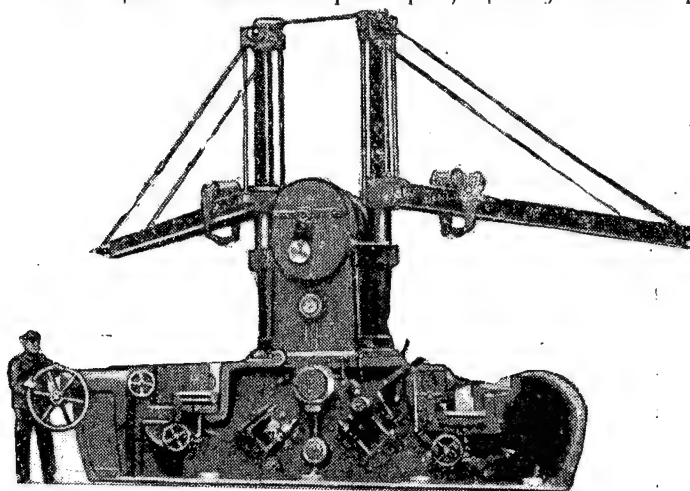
Горизонтальный комбинированный биметаллический и правильный пресс
